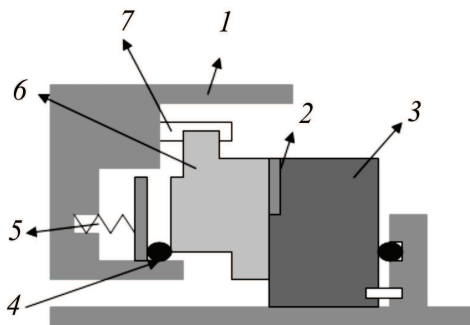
Схема конструкции уплотнительной пары газодинамического торцового уплотнения: 1 – корпус; 2 – канавки; 3 – вращающееся кольцо (седло); 4 – вторичное уплотнение; 5 – система пружин; 6 – невращающееся кольцо (торец); 7 – фиксатор от поворота
